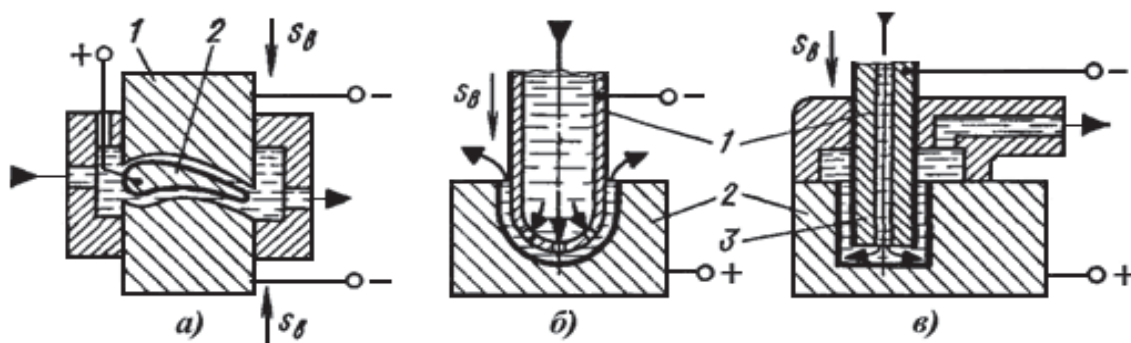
Схеми електрохімічної розмірної обробки: 1 – інструмент-електрод; 2 – заготовка; 3 – ізолятор
